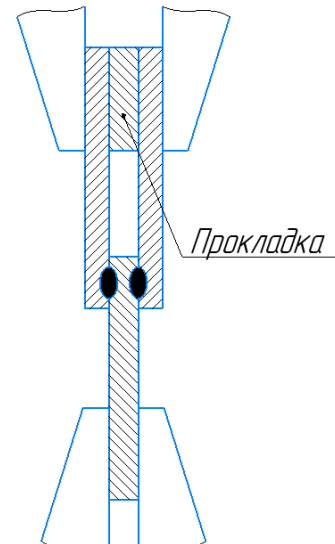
Схема зразка з двома зварними з'єднаннями
